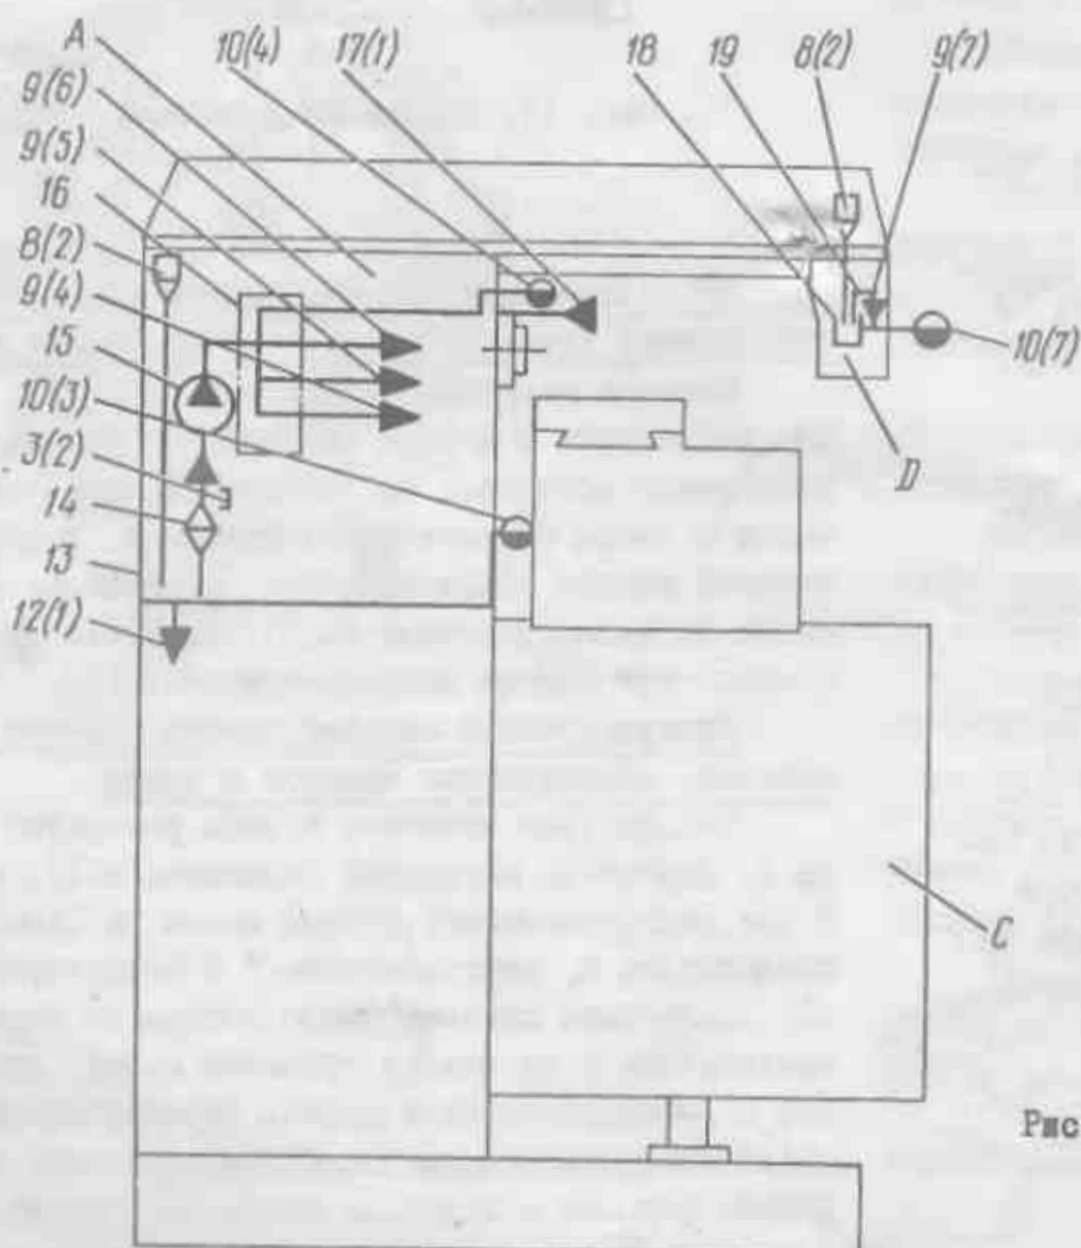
Принципиальная схема смазки станков 6Т80Г и 6Т80 (схему смазки привода С см. рис. 34)
